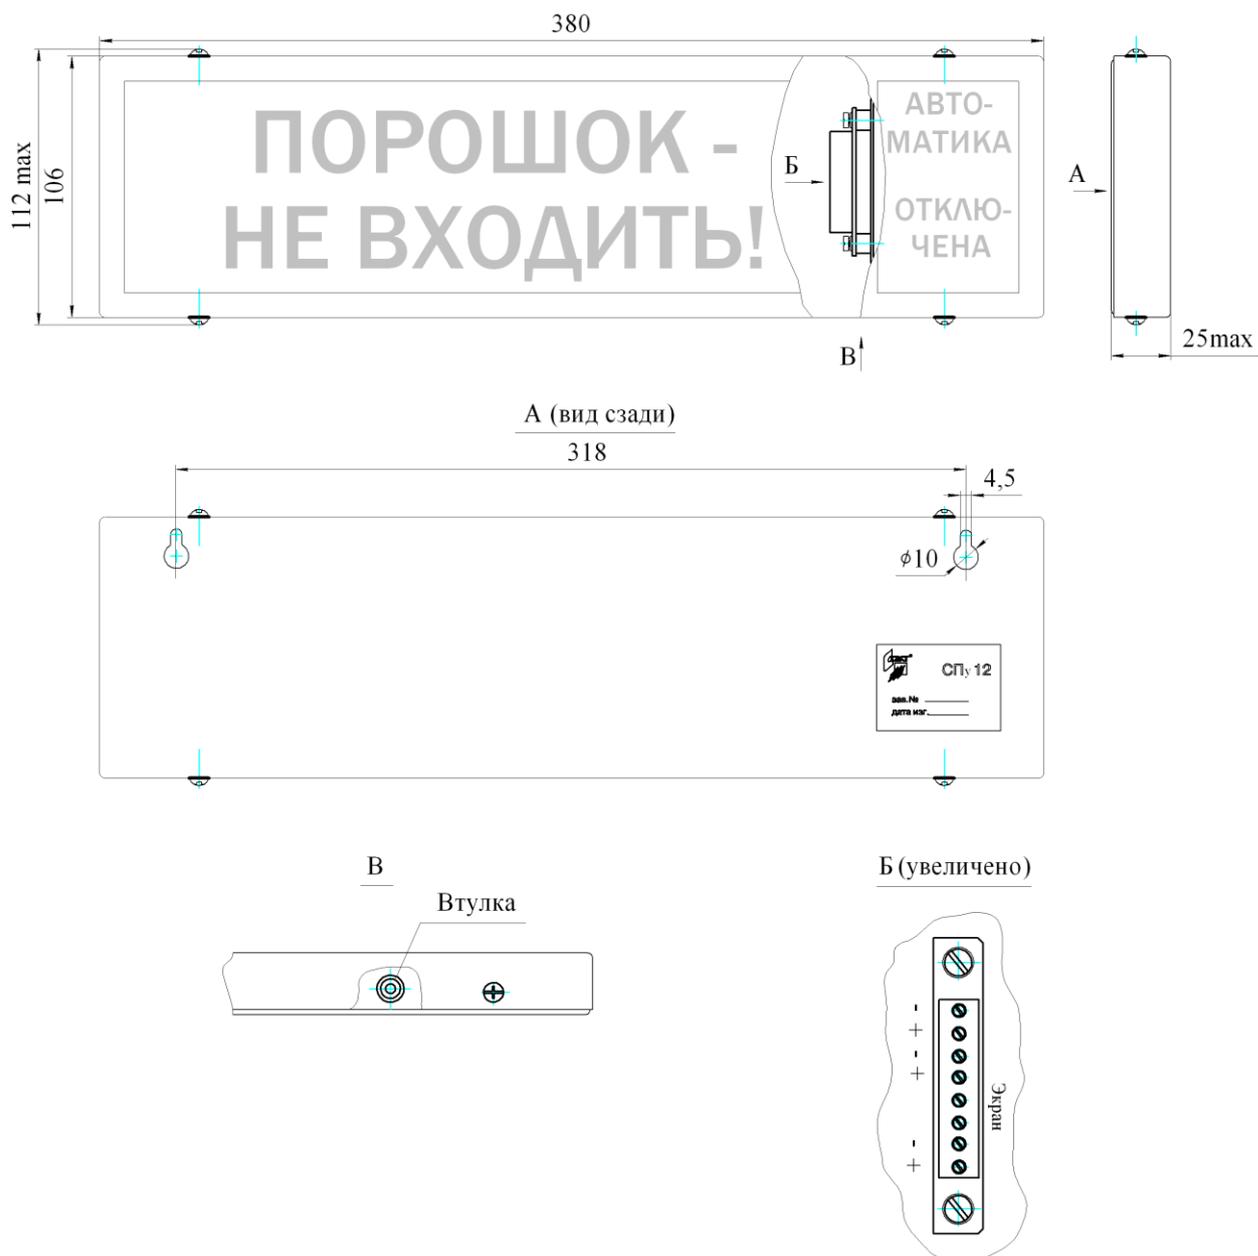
Оповещатель двойной СПу 12. Габаритный чертёж
